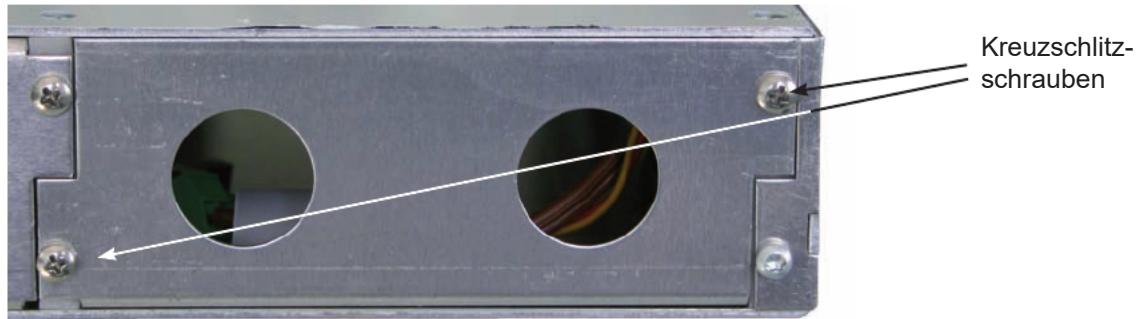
Position der Blindplatte im Auslieferzustand U 100
